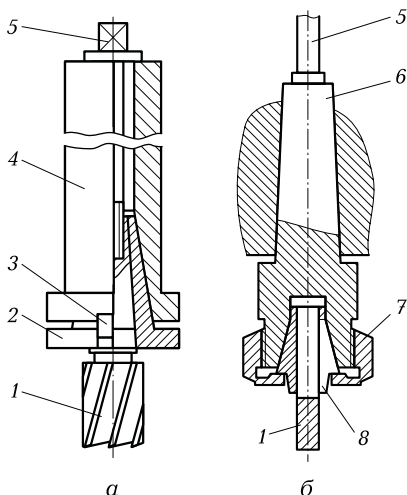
Схемы установки и закрепления на вертикально-фрезерном станке концевых фрез:
